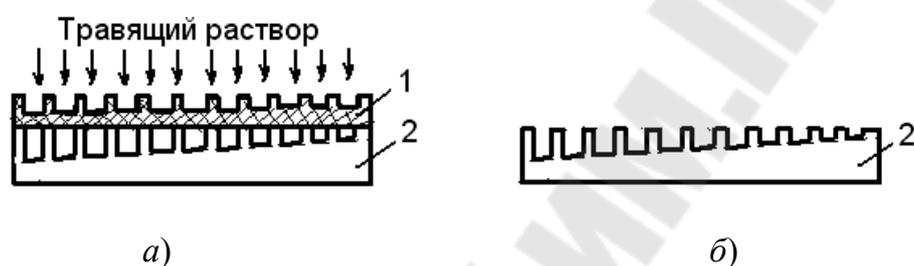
Схема изготовления формы глубокой печати пигментным способом
